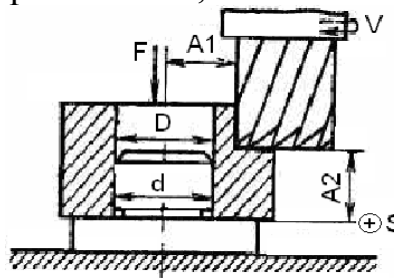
Схема фрезерування втулки (до задачі 1.3.)
